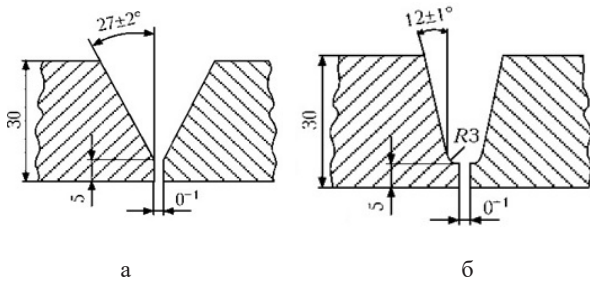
Схема обробки кромки для лазерного зварювання V-подібна (а) та U-подібна (б)
